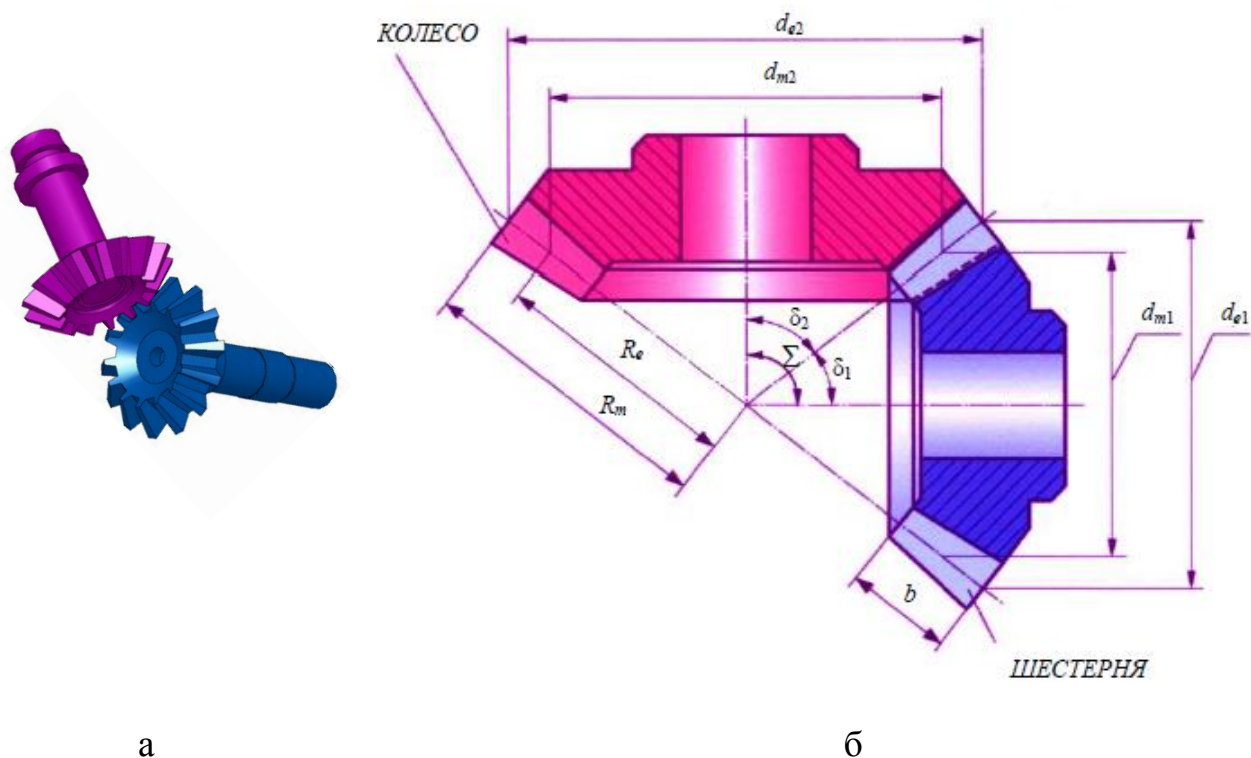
а - Схема конічної зубчастої передачі;
